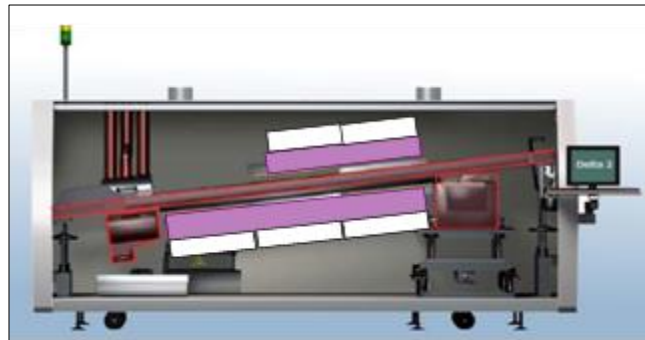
Muestra de la parte interna de la soldadora
